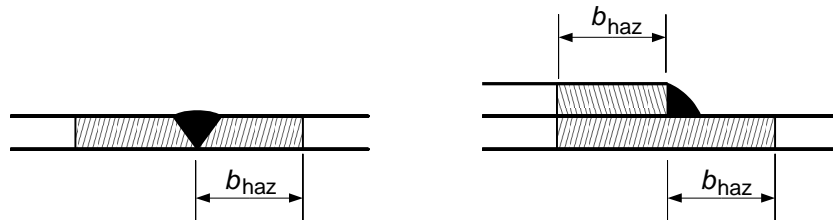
Estensione dell'HAZ in lamiere di strutture a guscio.
